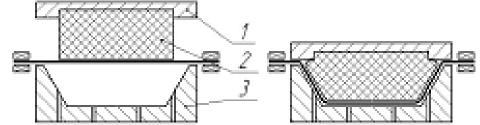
Схема штампования несопряженным штампом: 1 – обойма; 2 – эластичный пуансон; 3 – матрица
